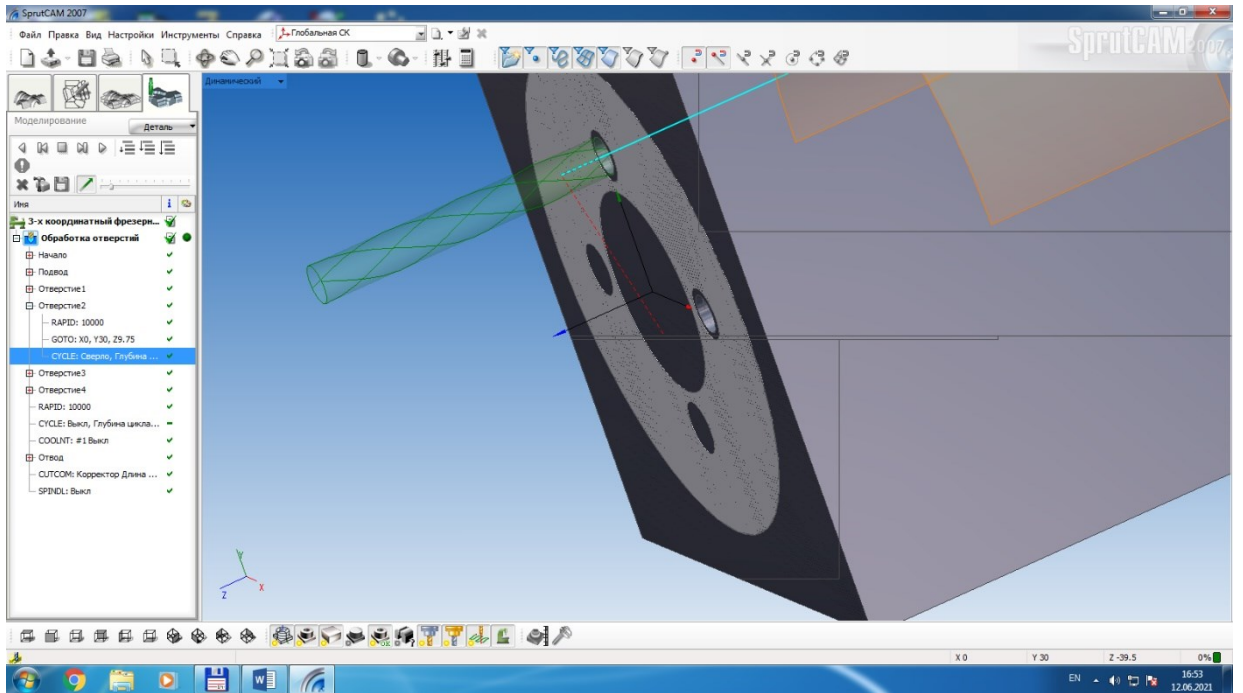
Заготовка, інструмент та оброблювані поверхні в системі SprutCAM.
